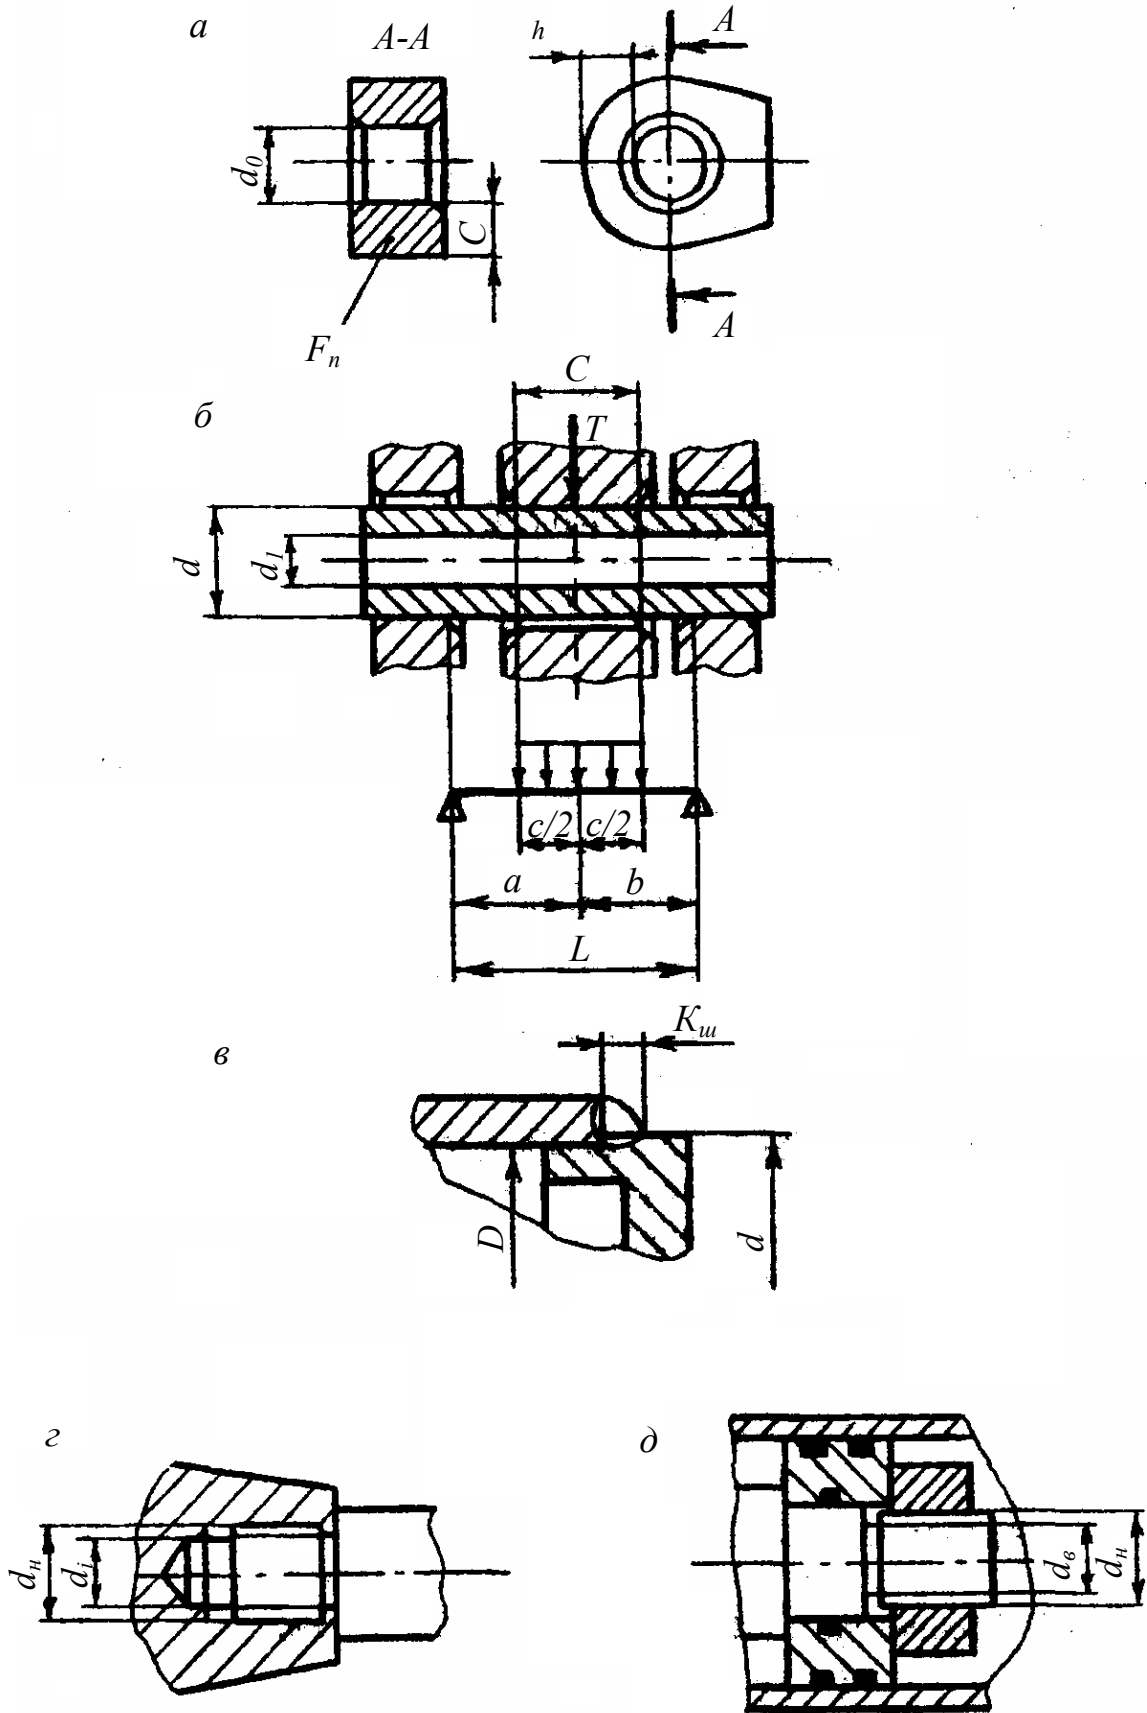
Расчетные схемы проушины, пальцев, сварных швов и резьб
